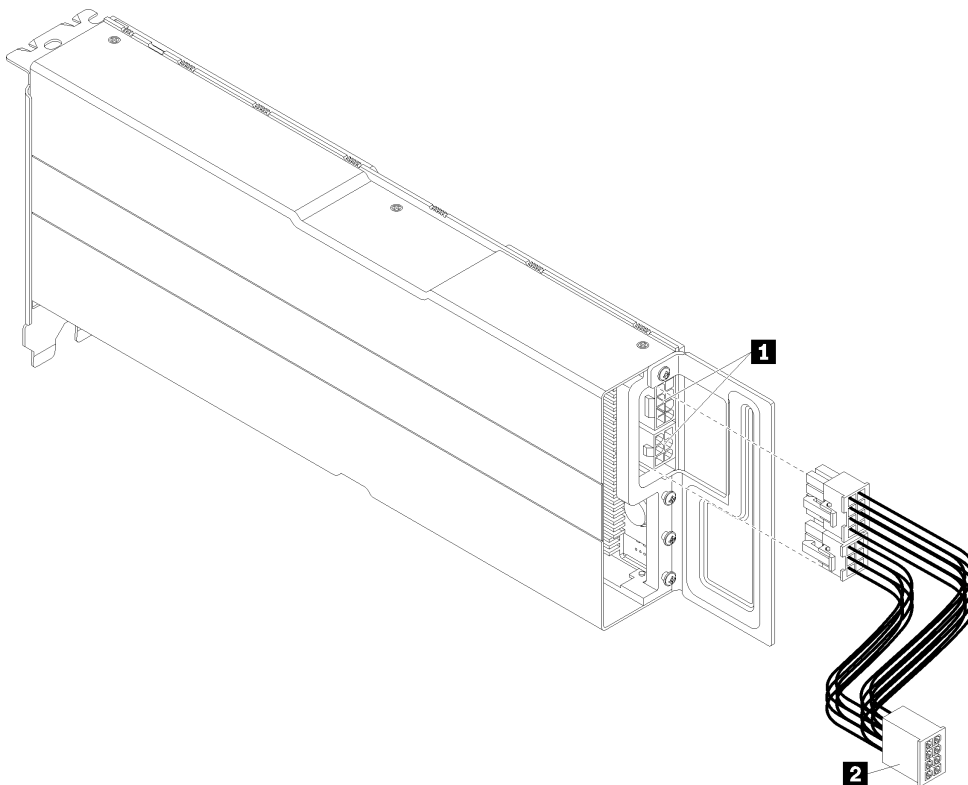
Collegare il cavo di alimentazione a Y all'adattatore GPU
